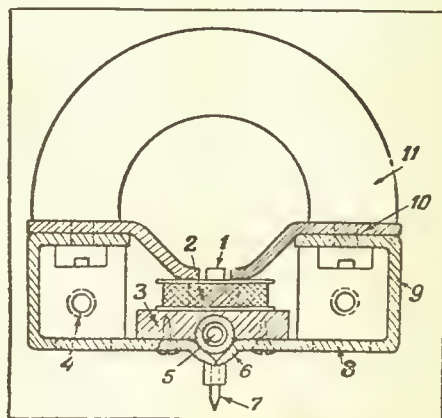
1 — вибратор лопатки, 2 — катушка, 3 — планка (латунь), 4 — отверстие для крепления, 5 — отверстие для крепежного винта, 6 — резиновая трубка, 7 — игла, 8 — отверстие для отверстия, 9 — коробка магнитопровода, 10 — полюсные наконечники, 11 — магнит
